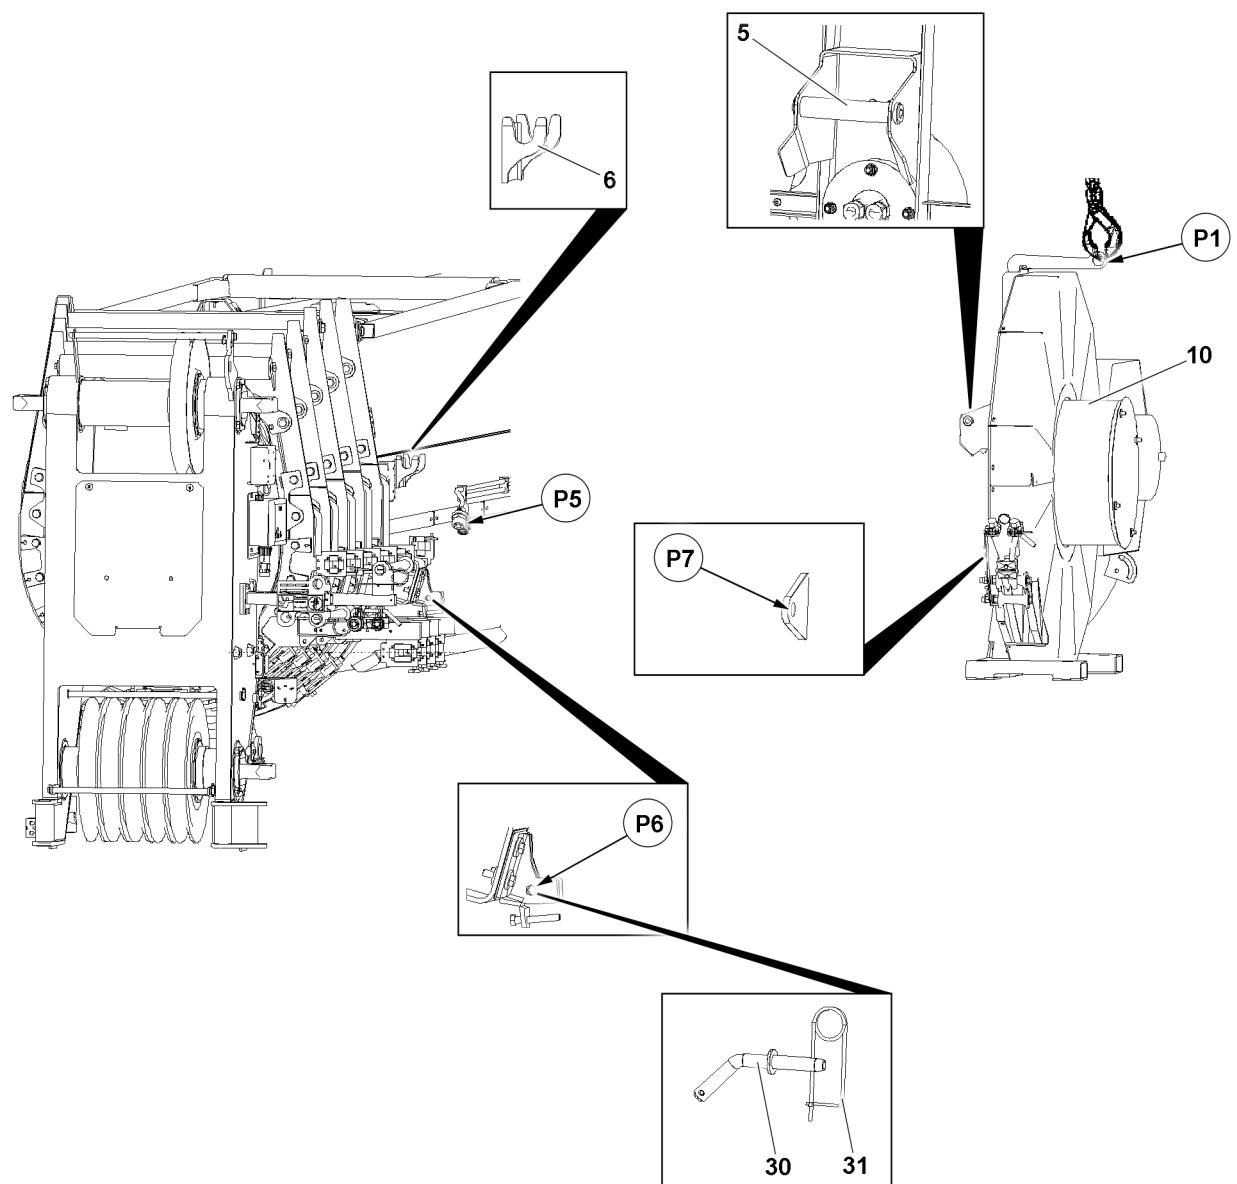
Montaje del tambor de mangueras hidráulicas
